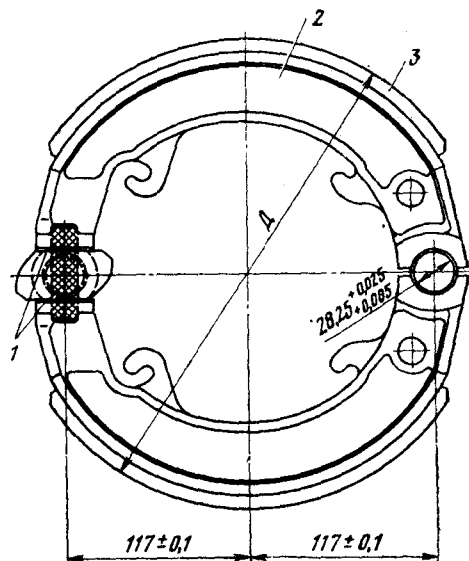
Размеры для установки колодок стояночного тормоза при механической обработке накладок:
